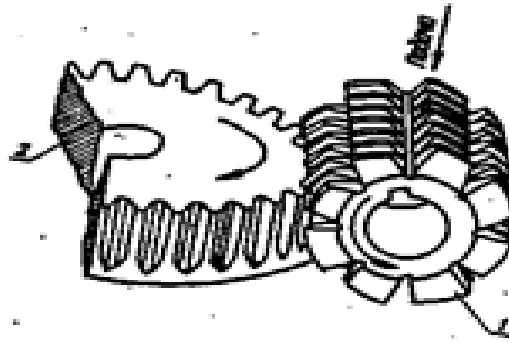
Схема нарезания зубчатого колеса червячной фрезой
